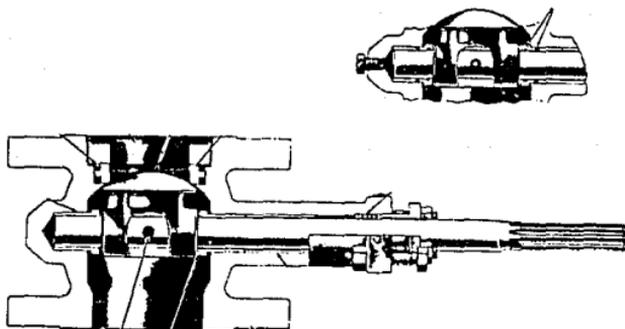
VALVULA DE DISCO EXCENTRICO
